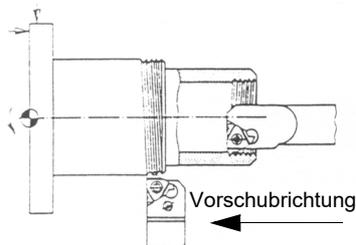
Rechtsgewinde bei Rechtslauf der Maschinenspindel
